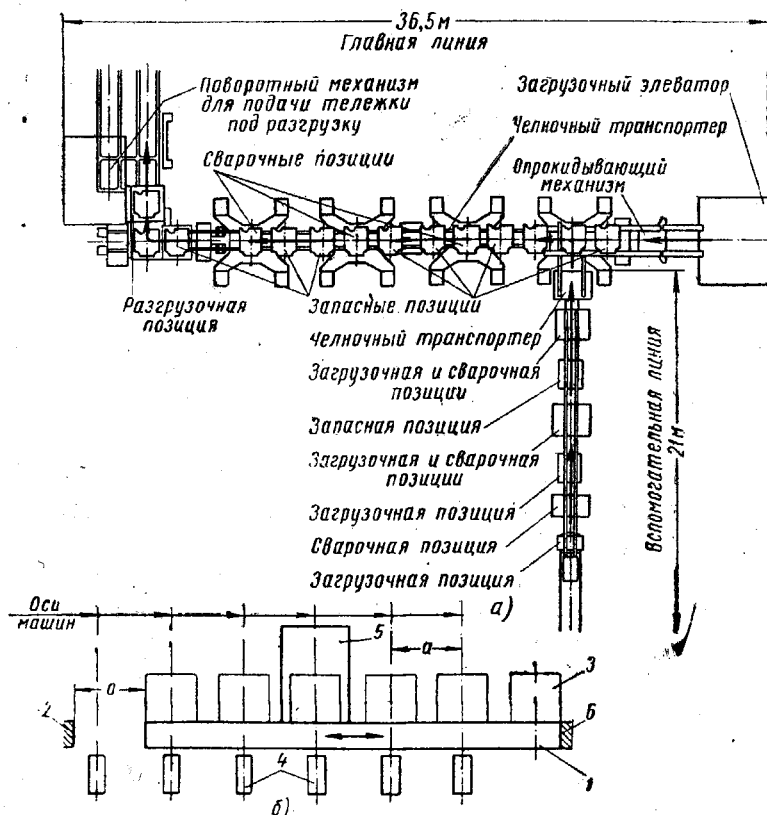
Схема многоточечной машины с перемещающимся порталом для сварки боковины вагона.
